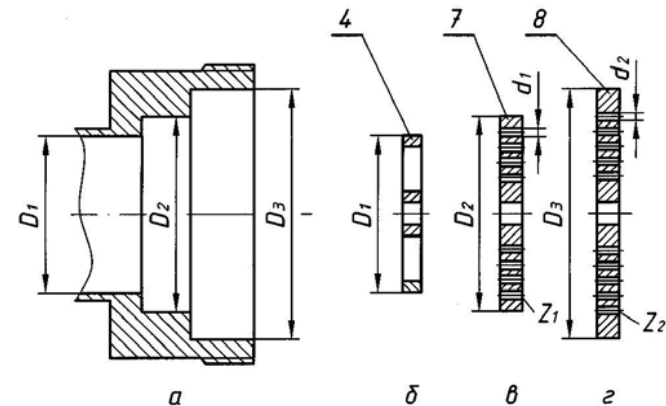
Схемы отдельных элементов волчка: а – схема рабочей камеры; б – схема подрезной решетки; в – схема приемной решетки; з – схема выходной решетки; 4 – решетка подрезная; 7 – решетка приемная; 8 – решетка выходная; D_1 – наружный диаметр подрезной решетки; D_2 – наружный диаметр приемной решетки; D_3 – наружный диаметр выходной решетки; d_1 – диаметр отверстий приемной решетки; d_2 – диаметр отверстий выходной решетки; Z_1 – количество отверстий в приемной решетке; Z_2 – количество отверстий в выходной решетке
